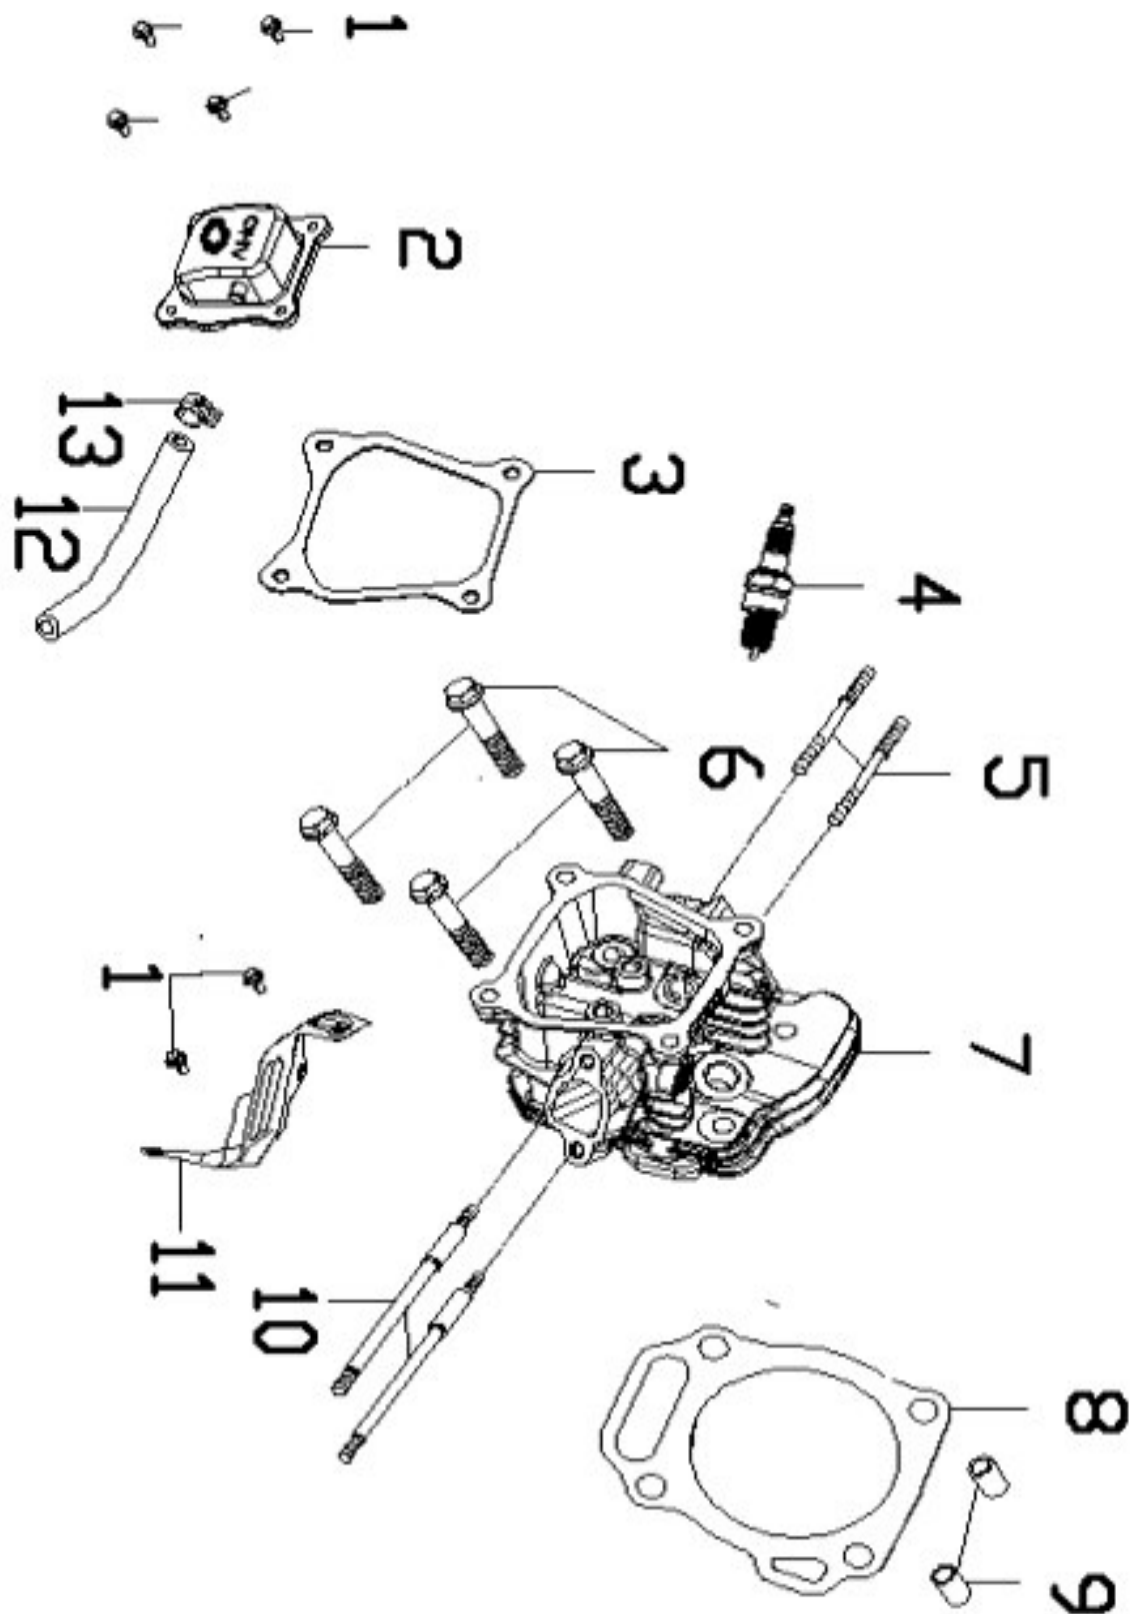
Ersatzteilzeichnung 2 - Zylinder Kopf
